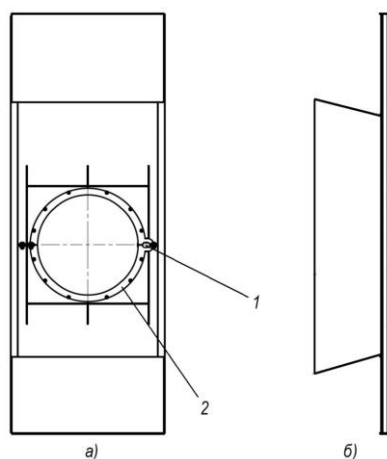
Уплотнительная коробка (а) и подвижный щит горелки (б)
